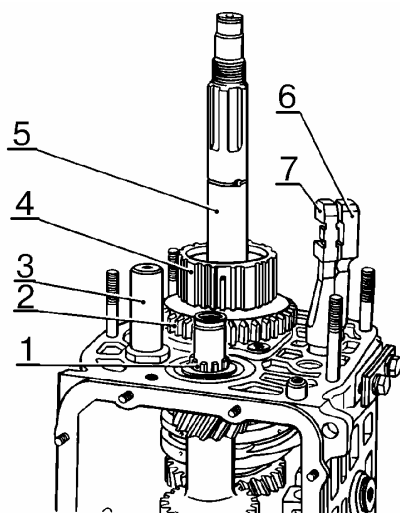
Снятие ведомой шестерни заднего хода и ступицы муфты синхронизатора V передачи:
